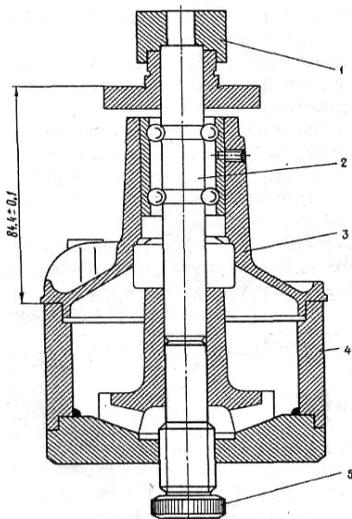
Напрессовка крыльчатки на валик насоса приспособлением А.60430
